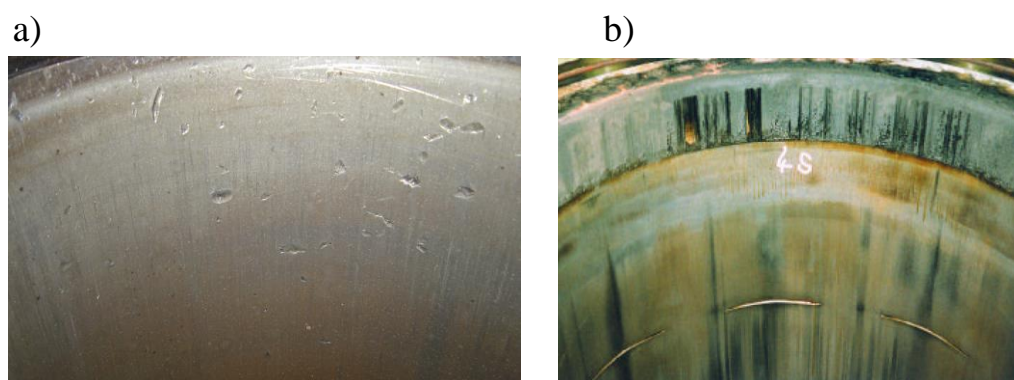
Uszkodzone elementy łożyska głównego wskutek zacierania czopa w panwi: a) półpanew, b) czop główny wału korbowego [29, 38]
